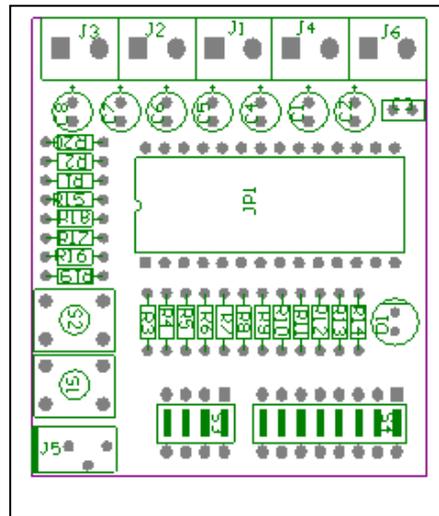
Esquema para el montaje de la Tarjeta Universal del ISD.
